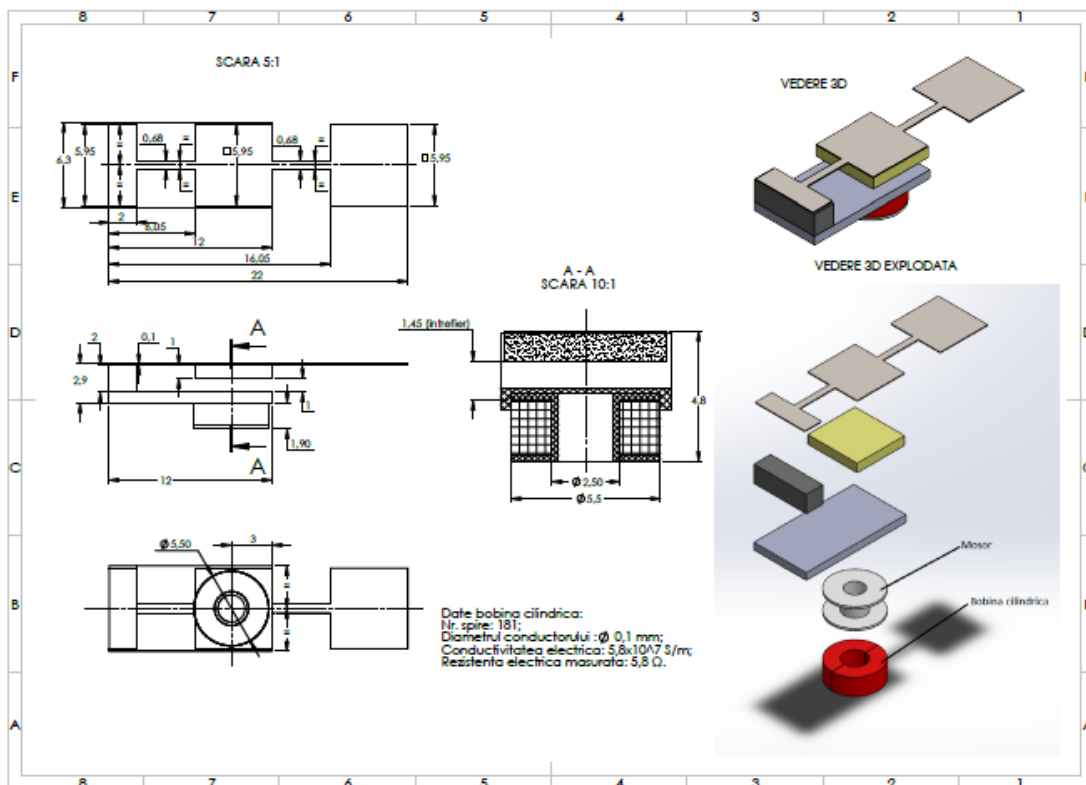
Construcția actuatorului cu magnet masiv și bobina cilindrică cu dublu cantilever.
